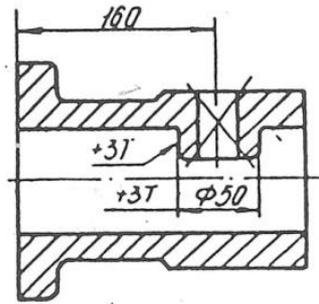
Обозначение неотливаемых отверстий на чертеже отливки
